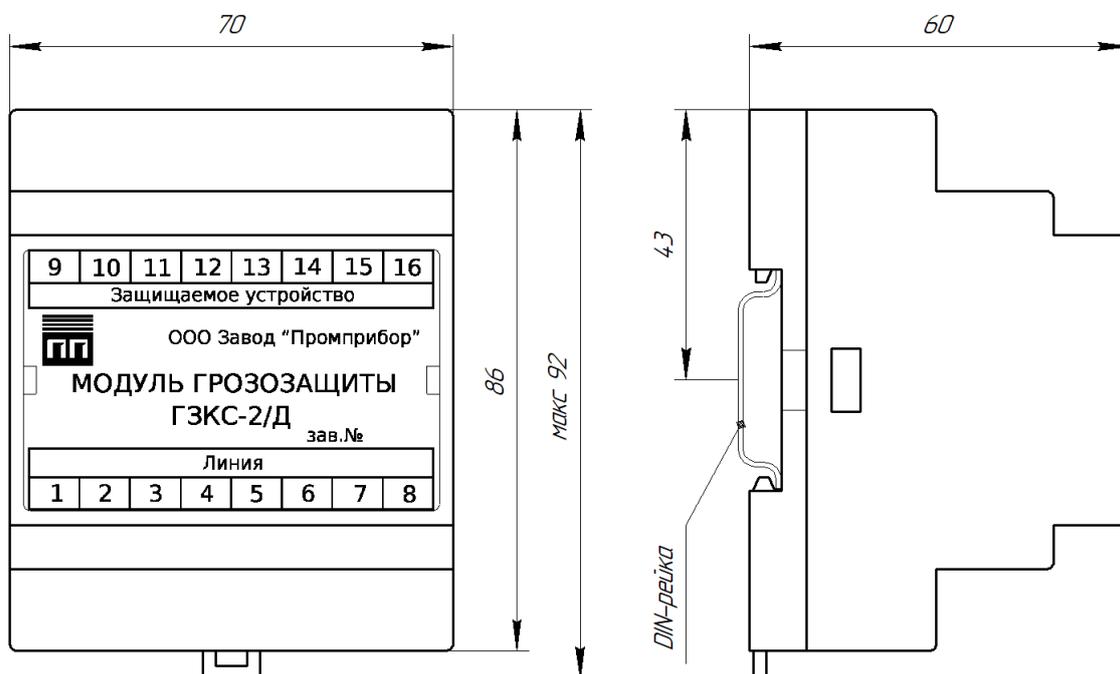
Габаритные и установочные размеры модуля грозозащиты
